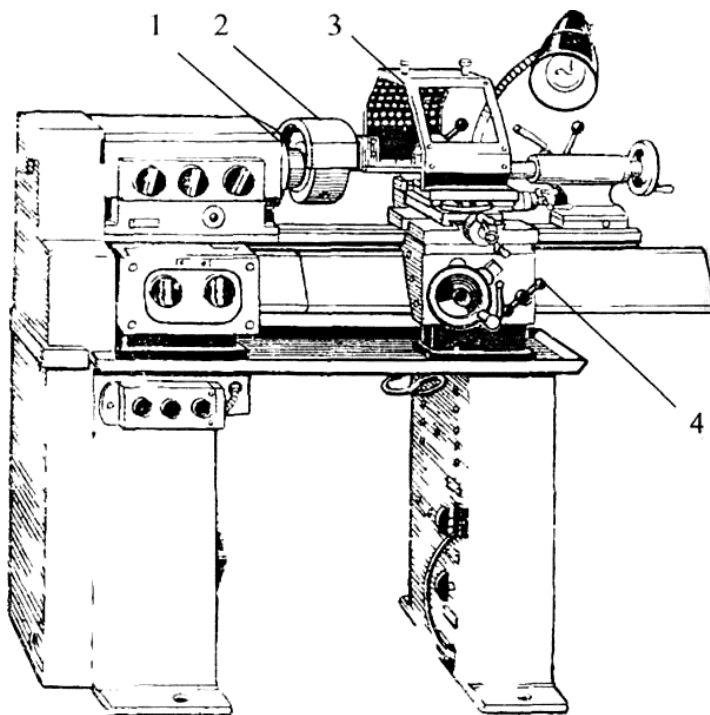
Защитные устройства токарно-винторезного станка.
